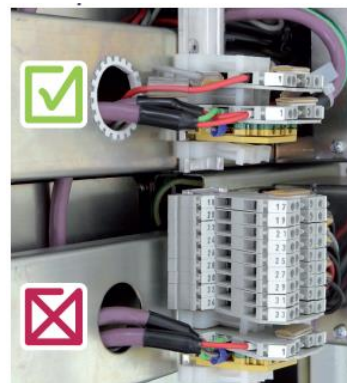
Passagem incorreta de cabos (esquerda); Proteção da passagem de cabos (direita)
